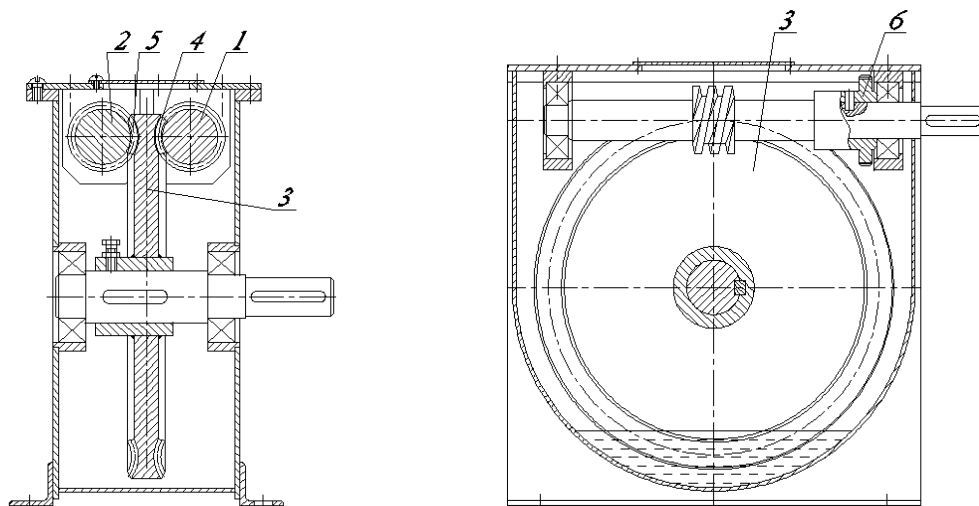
Редуктор на основе двухвенцовой червячной передачи
